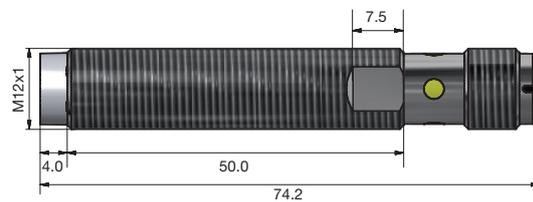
Lange Ausführung, bündiger Einbau, Kabel
